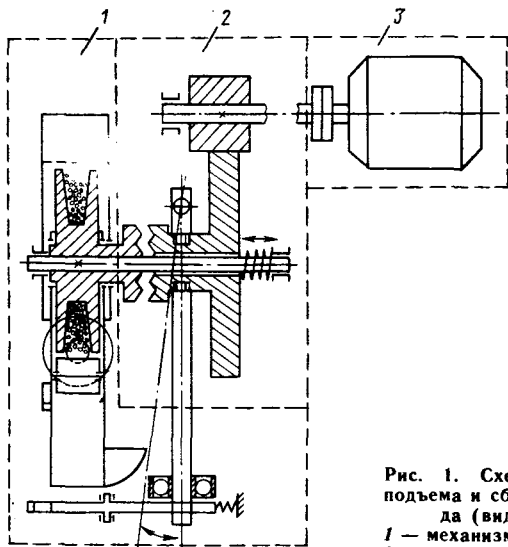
Схема механизма подъема и сбрасывания зонда (вид сверху): 1 — механизм зондирования; 2 — редуктор; 3 — привод
